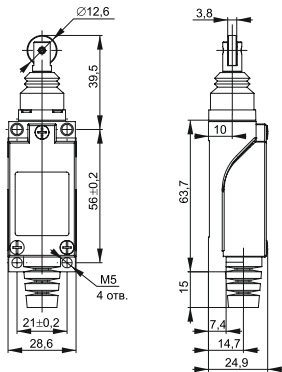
Габаритные, установочные размеры концевых выключателей
